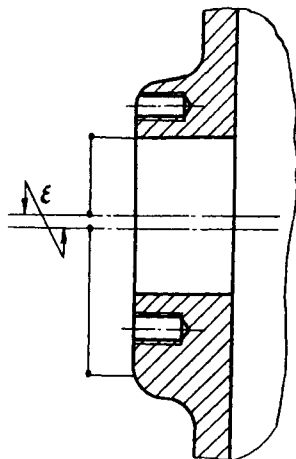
Связь отверстий под опоры валов в корпусных деталях с контурами поверхностей бобышек
